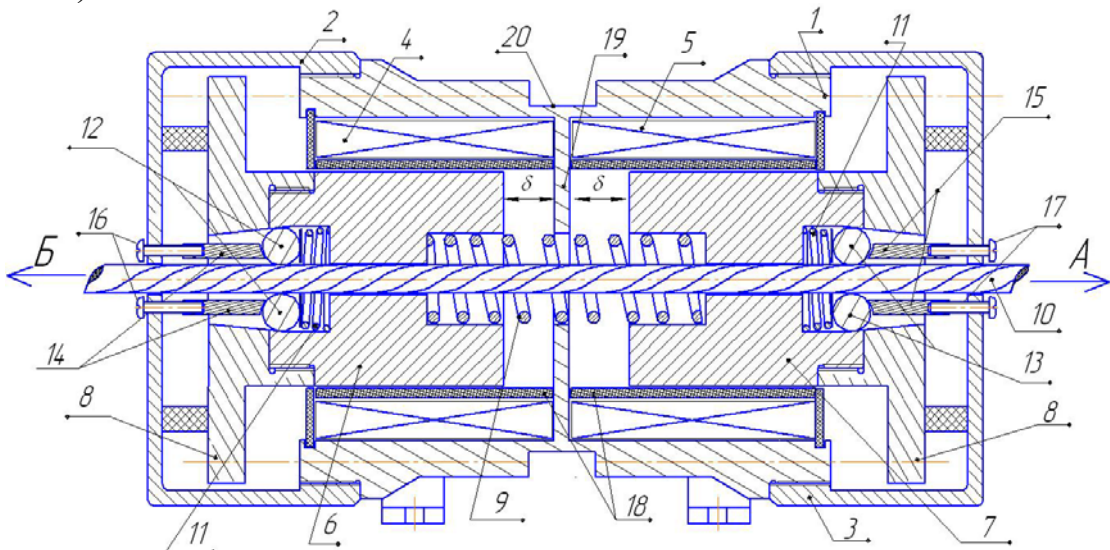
Конструкция реверсивного ЛЭМД со сферическими заклинивающими элементами: 1 – цилиндрический статор; 2, 3 – крышки; 4, 5 – обмотки; 6, 7 – комбинированный якорь; 8 – дисковая часть якоря; 9 – возвратная пружина; 10 – исполнительный орган; 11 – пружины; 12, 13 – сферические заклинивающие элементы; 14, 15 – шток для фиксации положения сферических элементов; 16, 17 – регулировочные болты; 18 – направляющие; 19 – полюс-шайба; 20 – кольцевой прямоугольный паз.
